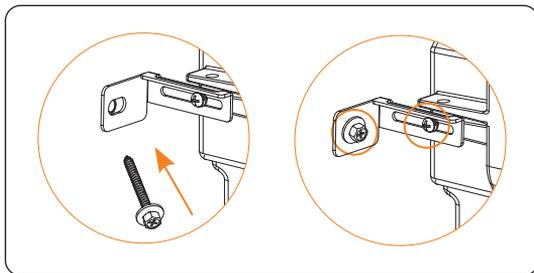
Die Blechschraube auf der linken Seite und die Schraube M5*10 sichern
